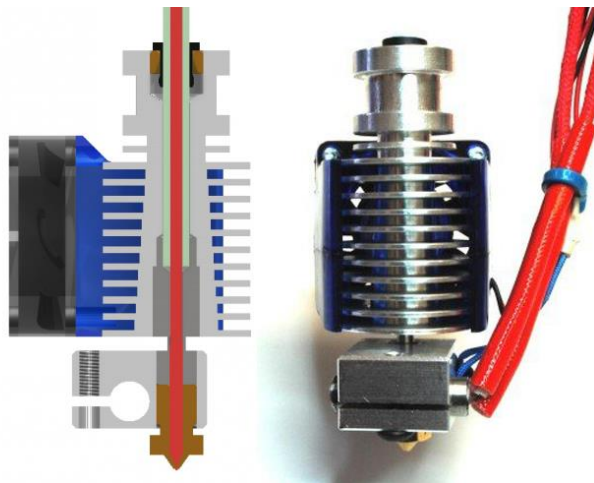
Різбова друкуюча головка v6 HotEnd 12В/24В [14]
